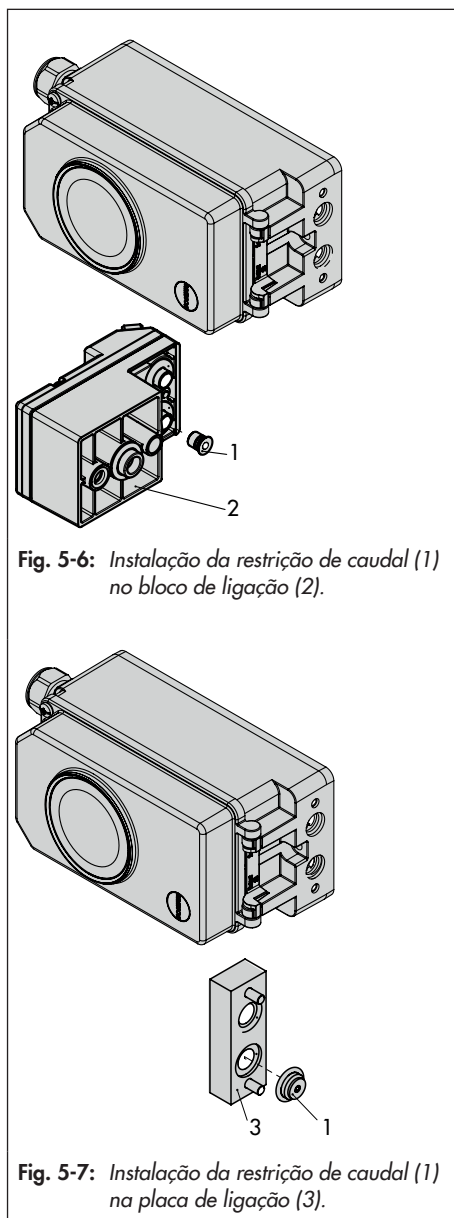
Instalação da restrição de caudal (1) no bloco de ligação (2).
